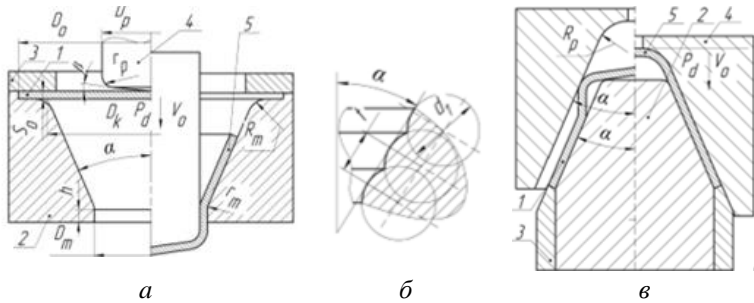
Схеми двохперехідного штампування конусного виробу: а – схема витягування, б – форма деформуючої поверхні матриці, в – схема обтиску
